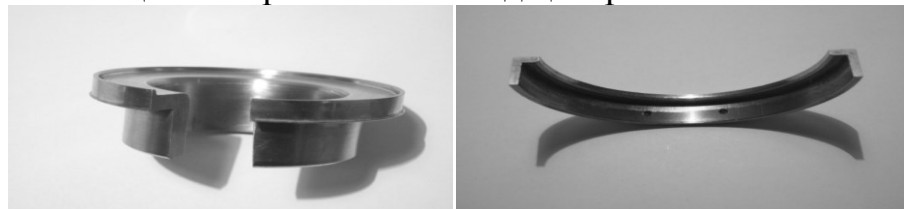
Заготовки з зовнішнім і внутрішнім буртом, отримані висадкою з цілеспрямованим зміщенням вершини кінцевого валка
